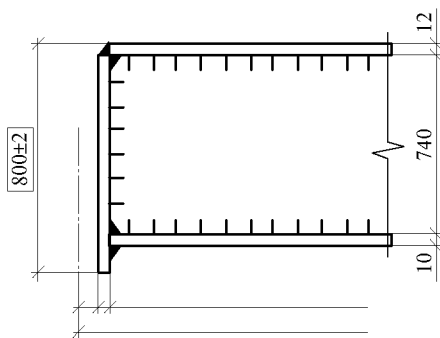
Пример простановки размеров на сварной балке
